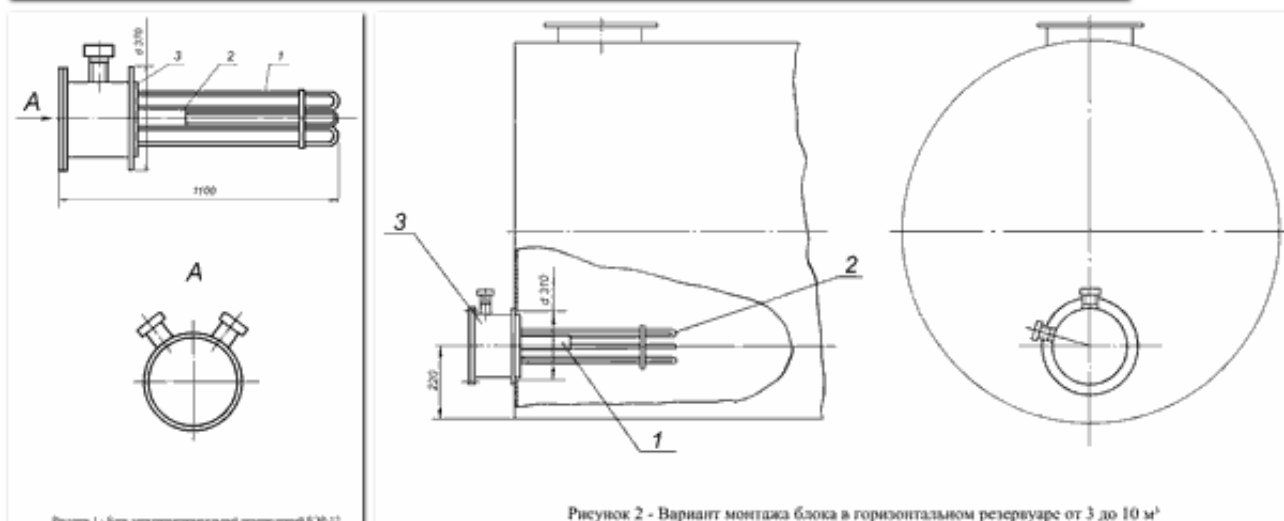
Блок электронагревательный резервуарный КЗ БЭР-12
